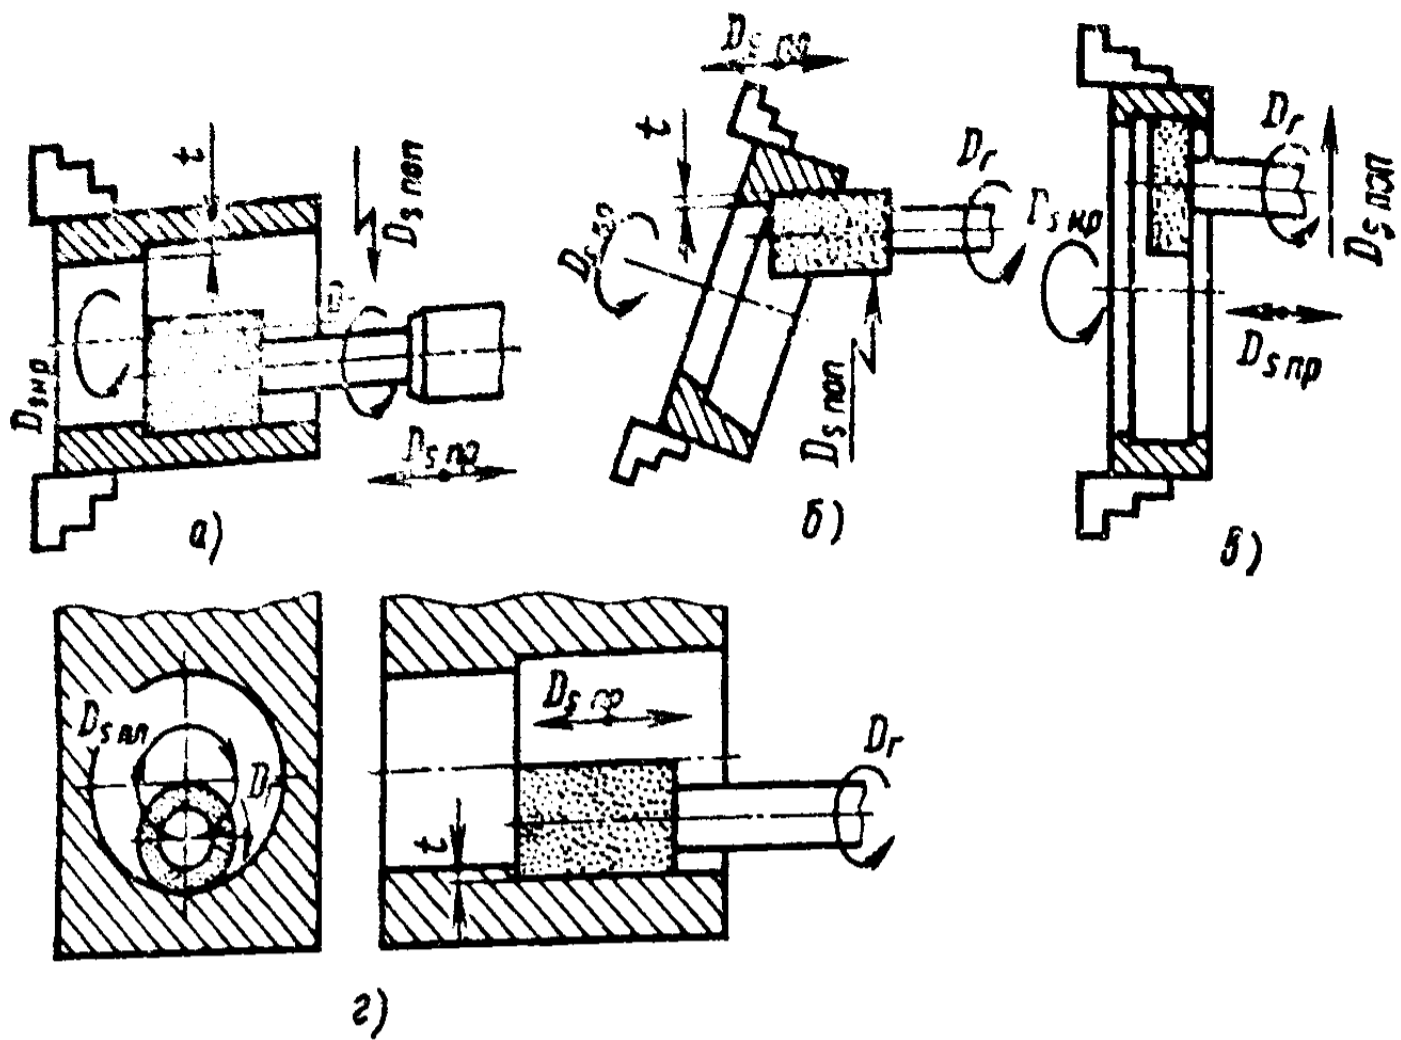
Схемы обработки заготовок на внутришлифовальных станках
